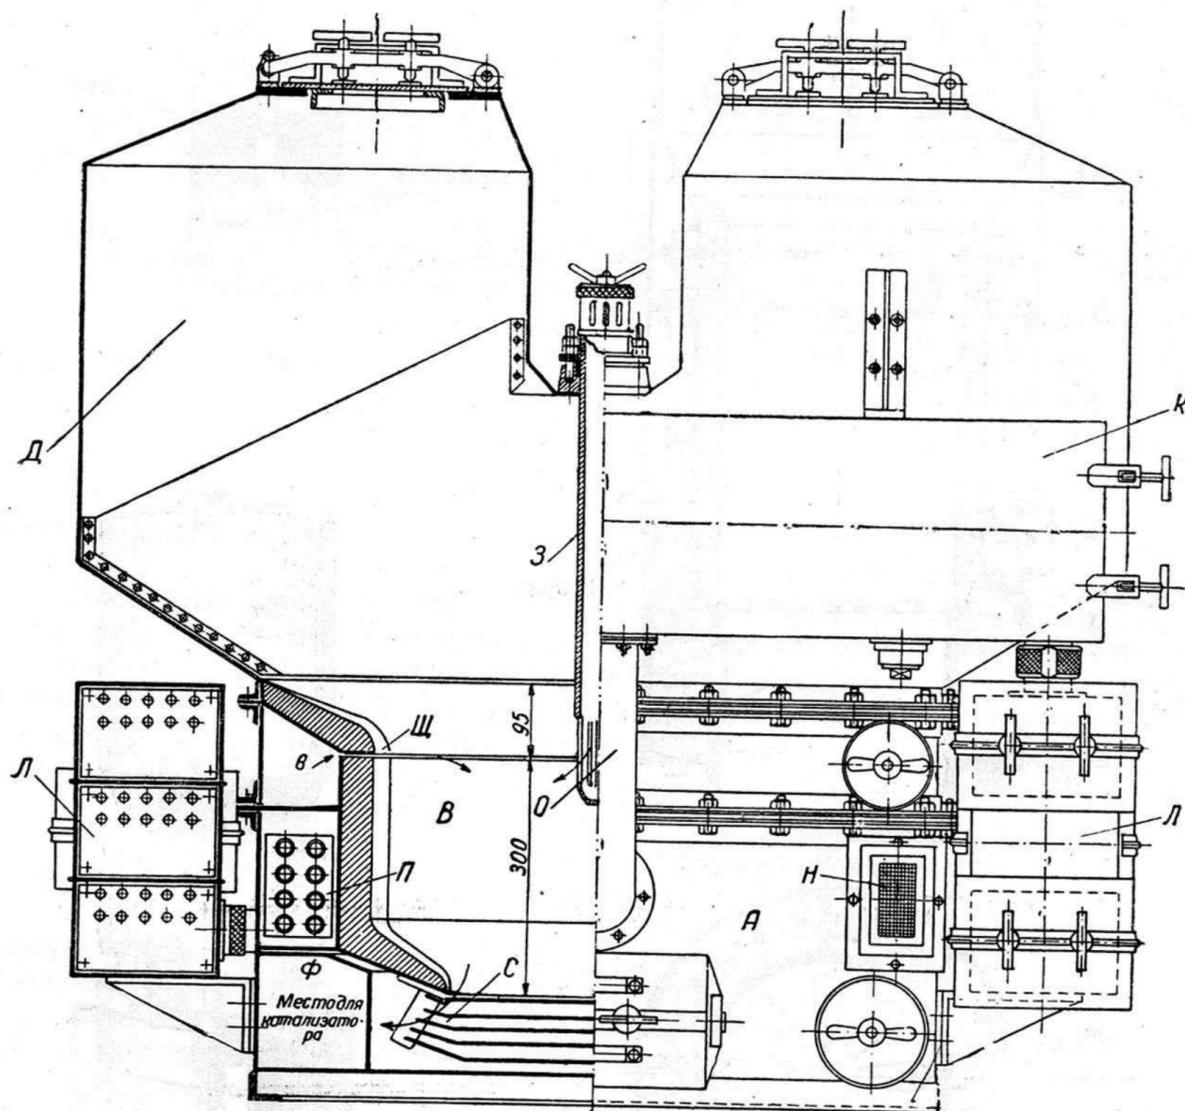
Газогенератор В-3. А—кожух шахты газогенератора; Д—бункер; В—топливник; С—колосниковая решетка; Щ—щель для всасывания основного воздуха; З—центральная подача воздуха; О—труба отсоса газа в очиститель; Ф—газосборник и катализаторы; П—подогреватель воздуха; Н—воздухоприемные отверстия подогревателей воздуха; К—первый грубый поверхностный очиститель; Л—вторые очистители, динамические
